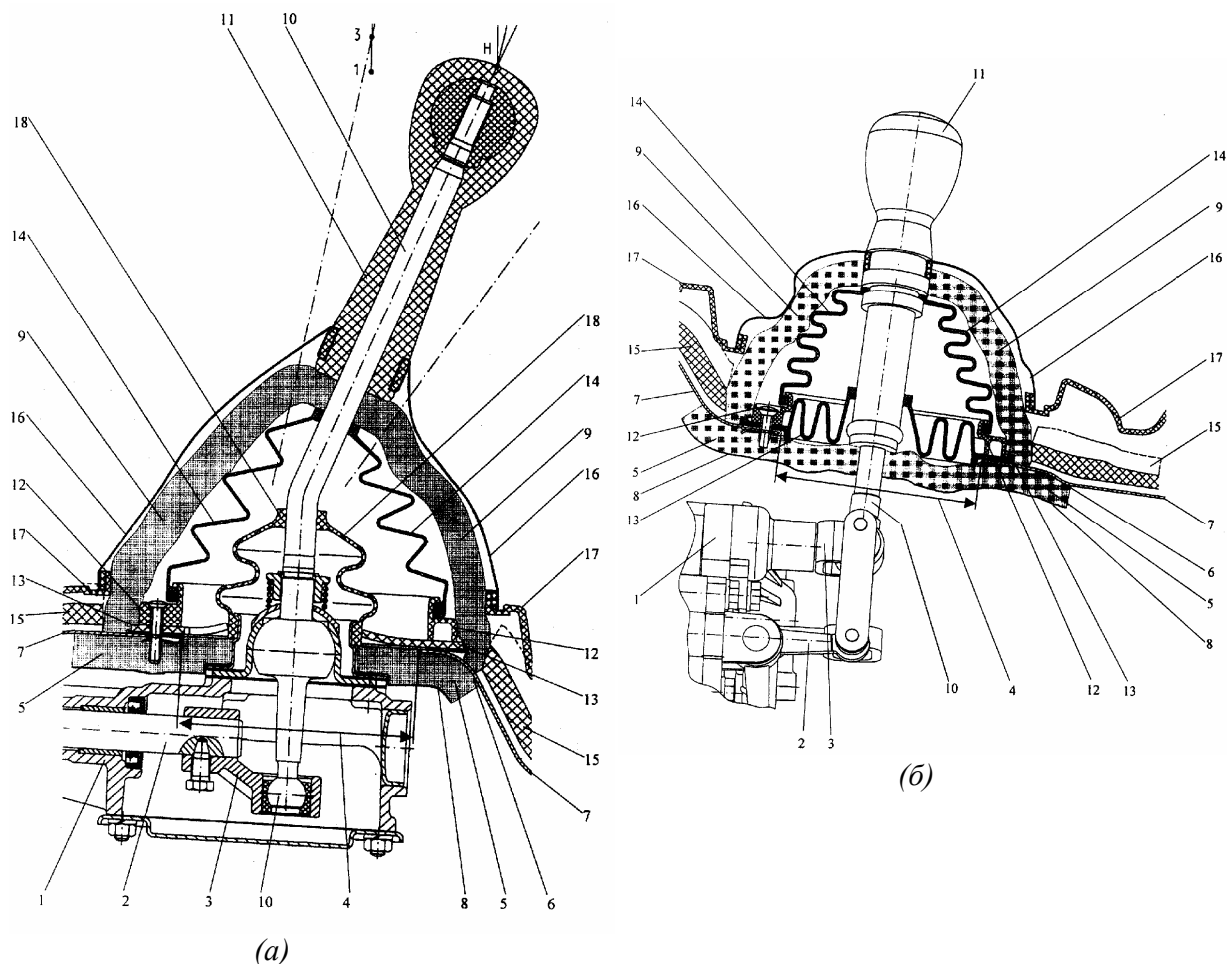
Фрагменты полноприводного автомобиля повышенной проходимости с раздельными рычагами переключения коробки передач (а) и раздаточной коробки (б):
